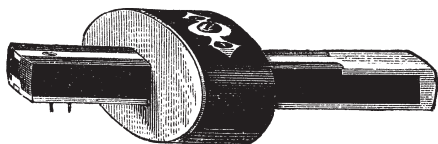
Рейсмус для разметки пазов с овальной колодкой
